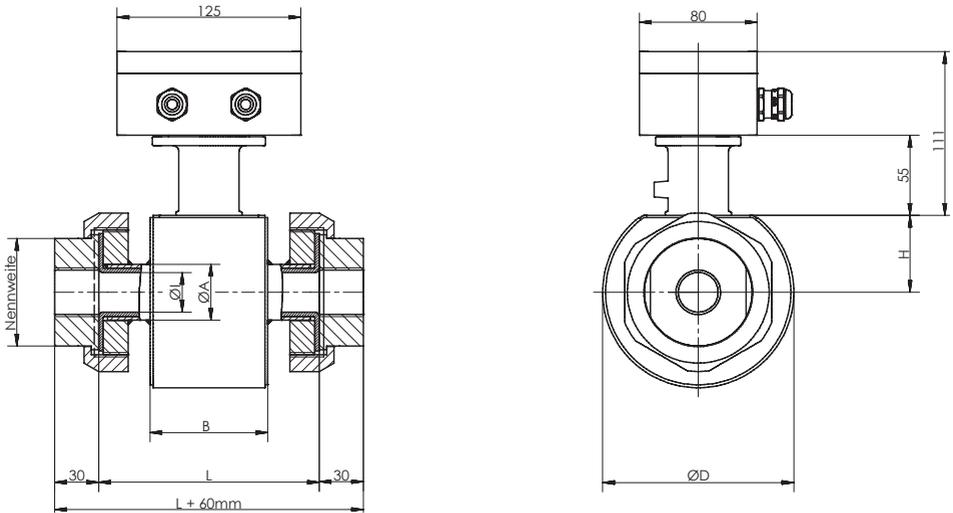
Maße Gewindeanschluss getrennte Bauform
